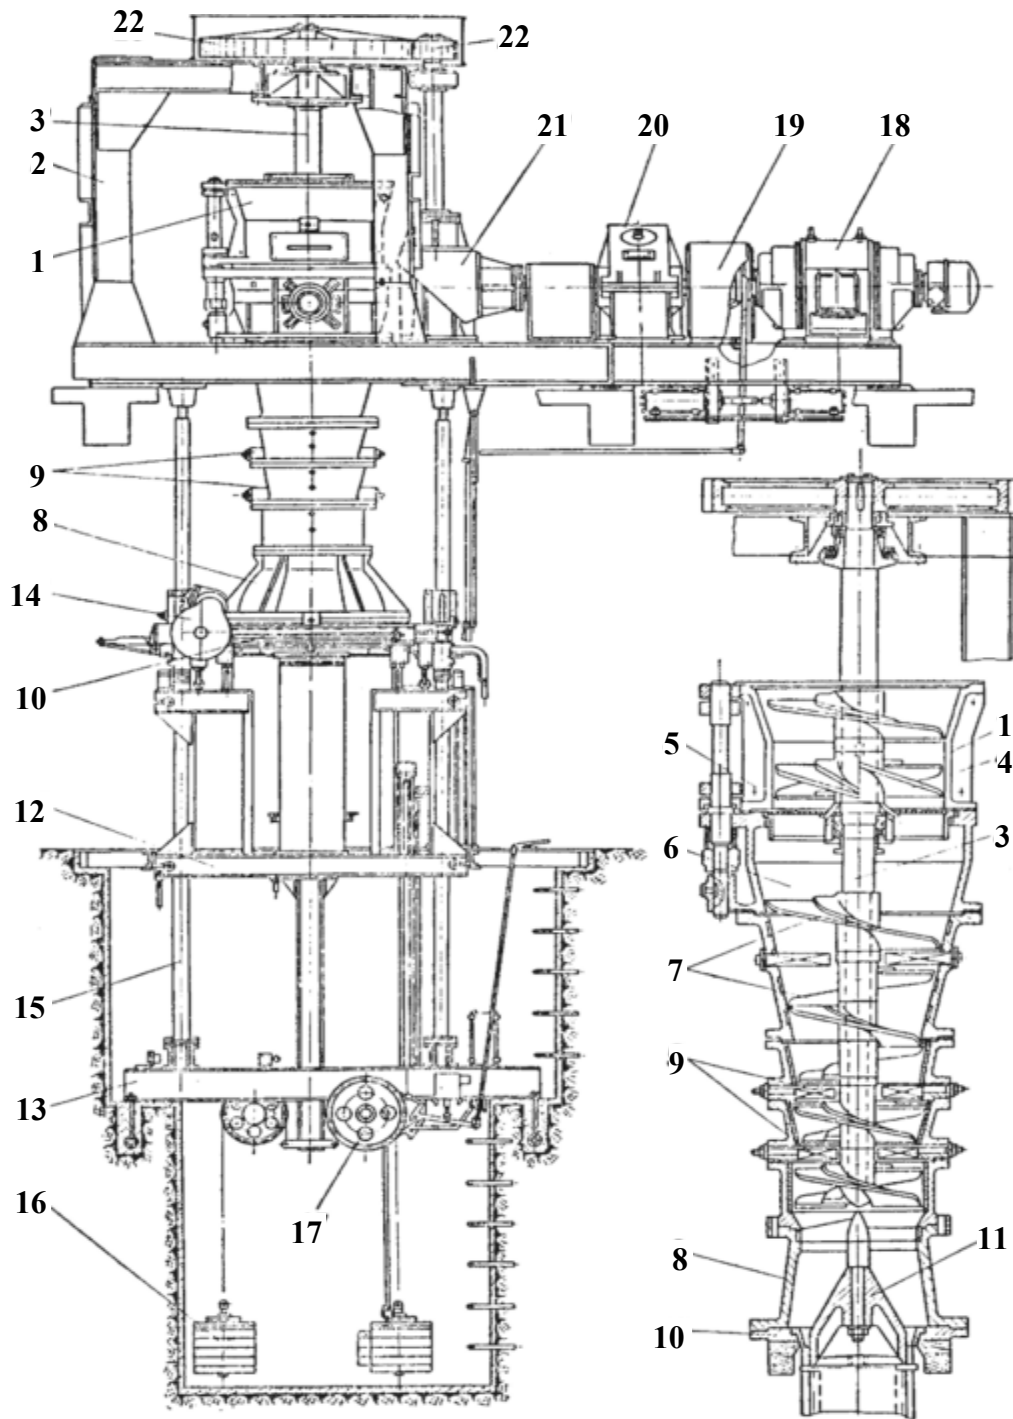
Вертикальний вакуумний прес: 1 – корпус; 2 – рама; 3 – вертикальний вал; 4 – подавальні шнеки; 5 – перфорована плита; 6 – вакуум-камера; 7 – шнеки; 8 – пресова головка; 9 – контрножі; 10 – змінні мундштуки; 11 – ковпаки; 12 – рухомий стіл; 13 – нерухомий стіл; 14 – відрізний пристрій; 15 – вертикальні колони; 16 – противаги; 17 – балансувальний пристрій; 18 – електродвигун; 19 – фрикційна муфта; 20 – редуктор; 21 – конічна зубчаста передача; 22 – циліндрична зубчаста передача
